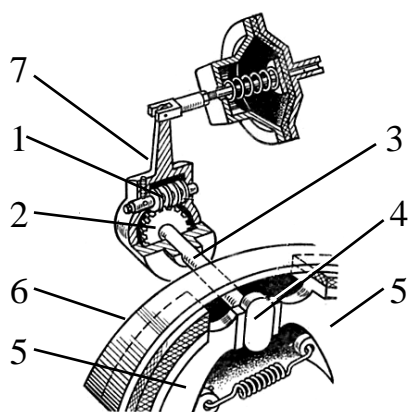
Регулировка барабанного тормозного механизма с кулачковым разжимным устройством: 1 – червяк; 2 – червячное колесо; 3 – вал; 4 – кулачок; 5 – тормозные колодки; 6 – тормозной барабан; 7 – корпус регулировочного механизма
